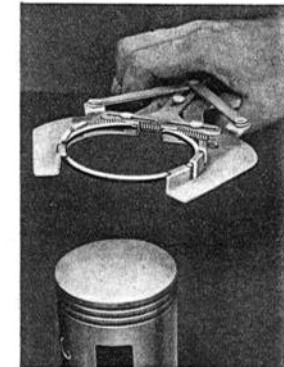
Abnehmen und Aufsetzen der Kolbenringe mittels Kolbenringzange Nr. 0162
